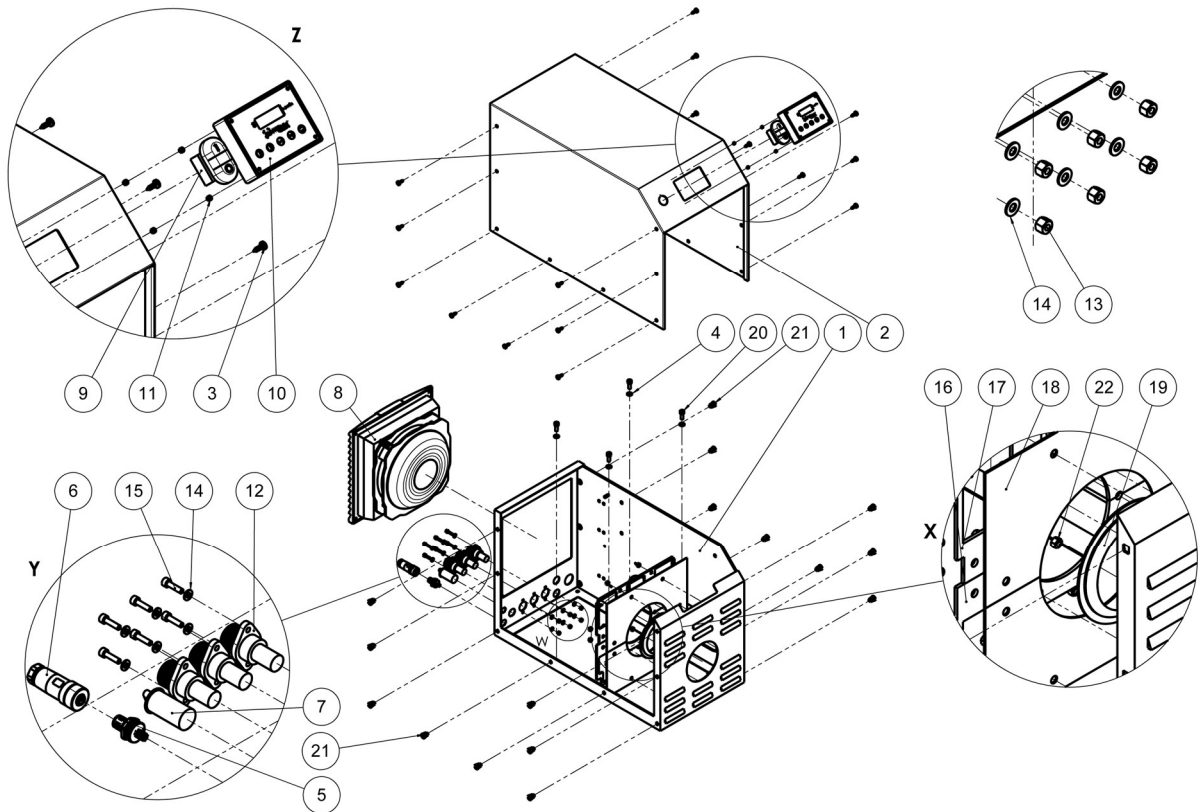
Baugruppe Gehäuse PQ44N-HT
